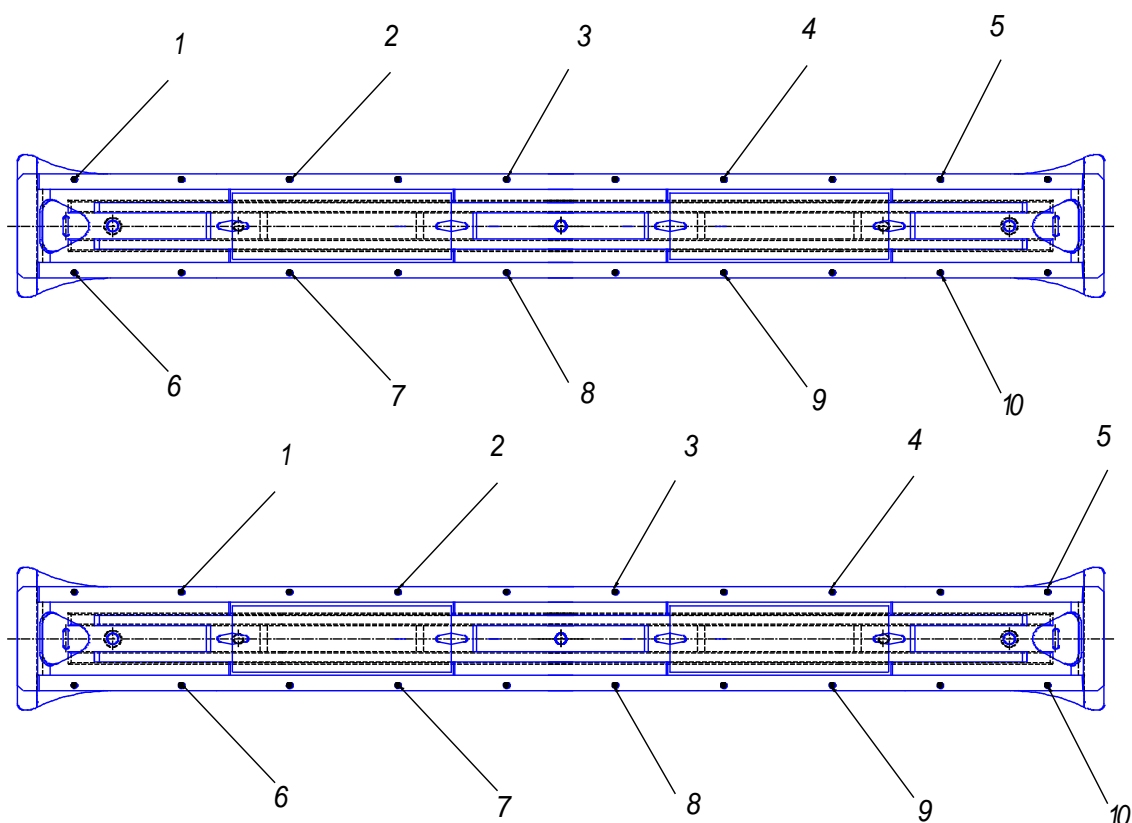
Простановка сварных точек сварочными пистолетами на МТМ
